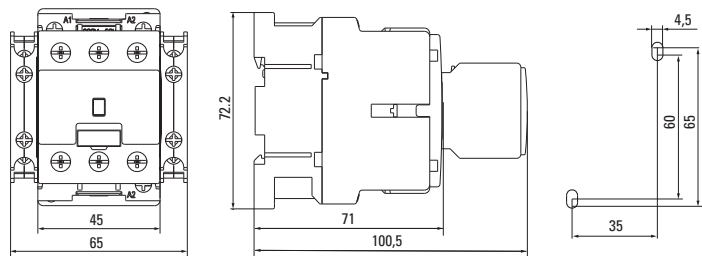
Габаритные и установочные размеры контакторов КМЗ 25А, КМЗ 30А
